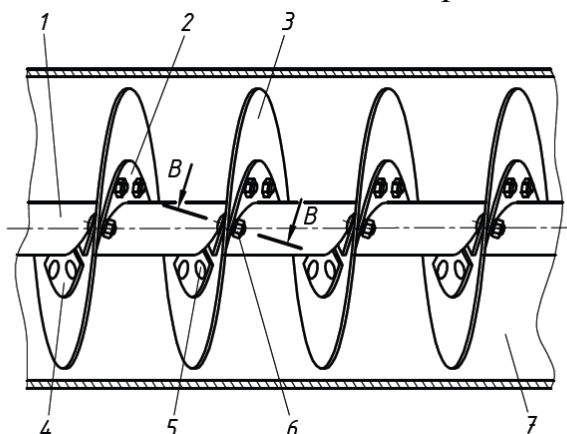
Конструкція шнека з еластичною гвинтовою поверхнею
